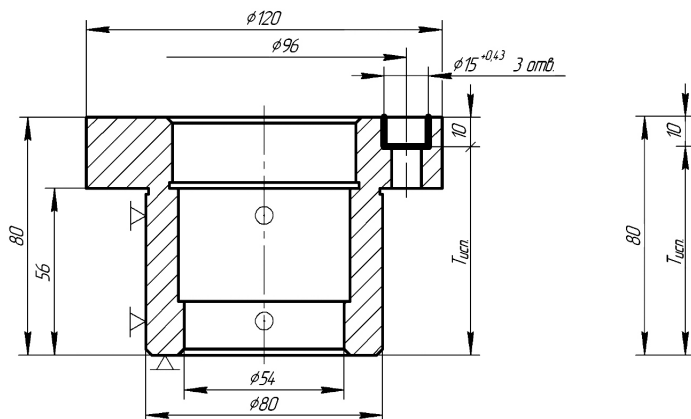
Операционный эскиз обработки и размерная цепь в случае базирования по торцу диаметром 80 и цилиндрической поверхности диаметром 80
